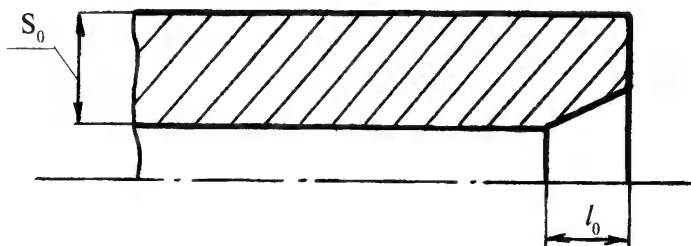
Форма поводковой части заготовки при толщине стенки $S_0 \leq 6$ мм
